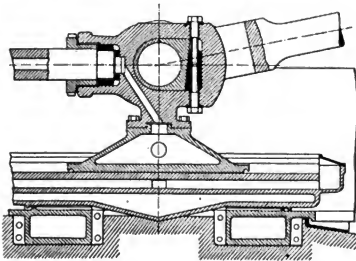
Befestigung der Kolbenstange im Kreuzkopf bei den Körtngmaschinen der Siegerner Maschinenbau-Akt.-Ges. in Siegen.
